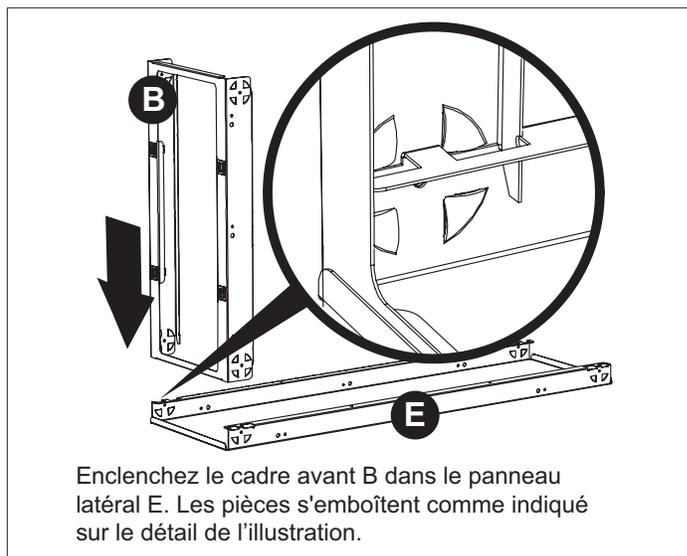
Assembler le cadre avant (B) sur le panneau latéral (E)
